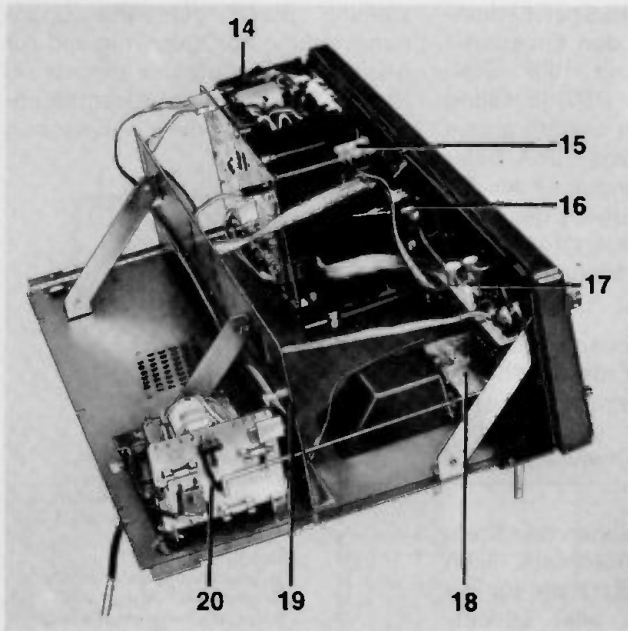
Rückansicht des CB 40. Die Anschlüsse zu den Köpfen sind von der Rückseite her gesteckt, um ohne Ausbau des Bausteines Messungen durchführen zu können.
